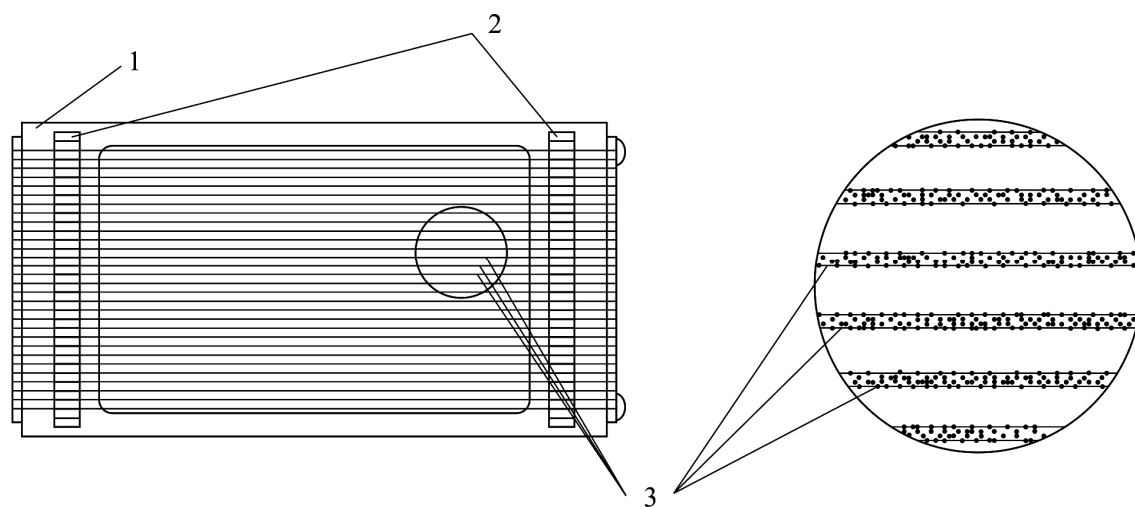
Інструмент для різання струнами із закріпленими алмазними зернами. 1 – інструмент; 2 – розмірні планки;
